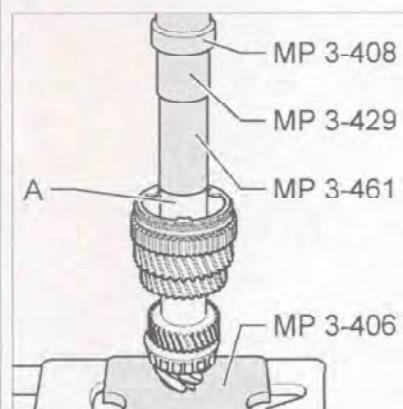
Напрессуйте внутреннюю обойму игольчатого подшипника шестерни 1-й передачи (A) до упора с помощью специального инструмента.
